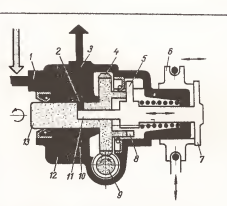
Схематичный разрез насоса: 1 — подача масла; 2 — пульт дозирования смеси; 3 — дроссель; 4 — регулирующая шестерня; 5 — плунжер; 6 — регулирующий шток; 7 — регулирующий шток; 8 — цилиндр; 9 — корпус; 10 — впуск масла; 11 — плунжер; 12 — масляный резервуар; 13 — распределитель.
